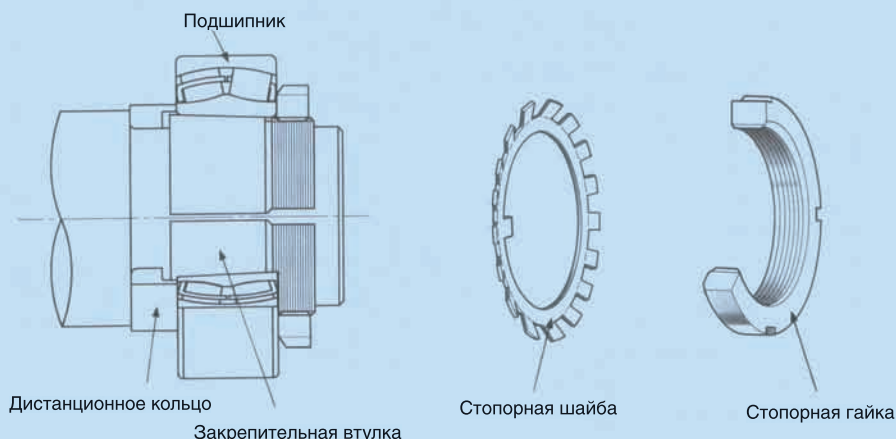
Установка стопорной шайбы по окончании регулировки зазора.
